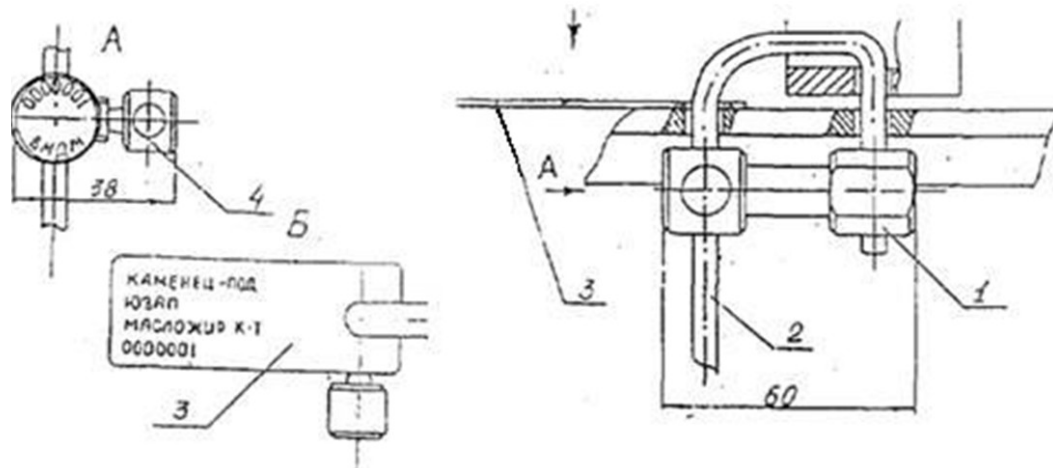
Запірно-пломбувальний пристрій "Варта-Універсал"
